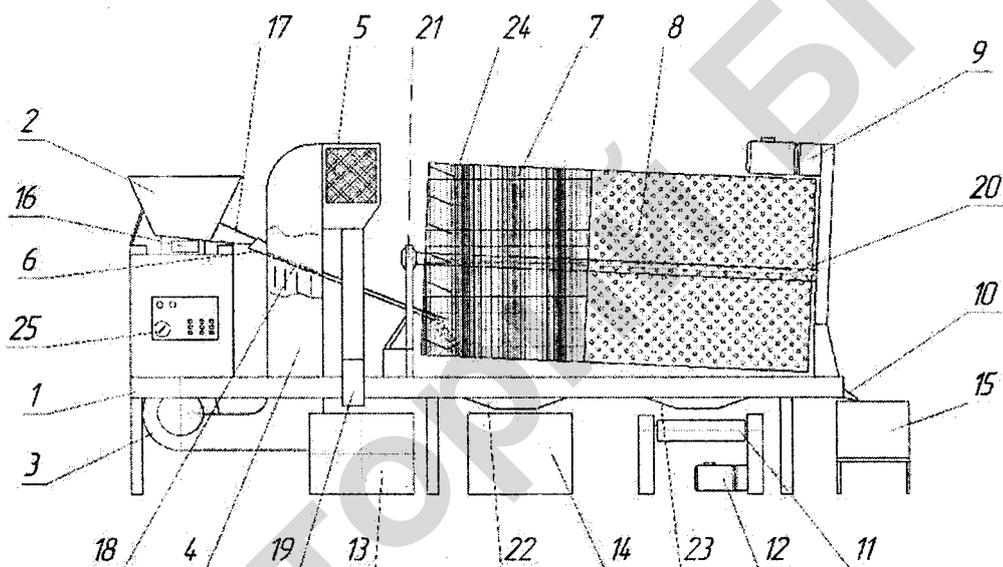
Конструктивная схема машины для очистки и сортировки ягод
